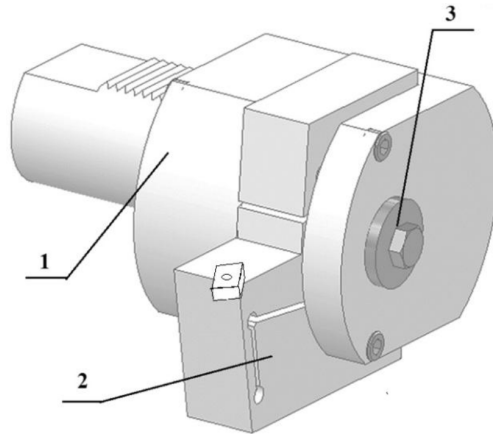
Загальний вигляд різцетримача з демпфером токарно-револьверного верстата, де
